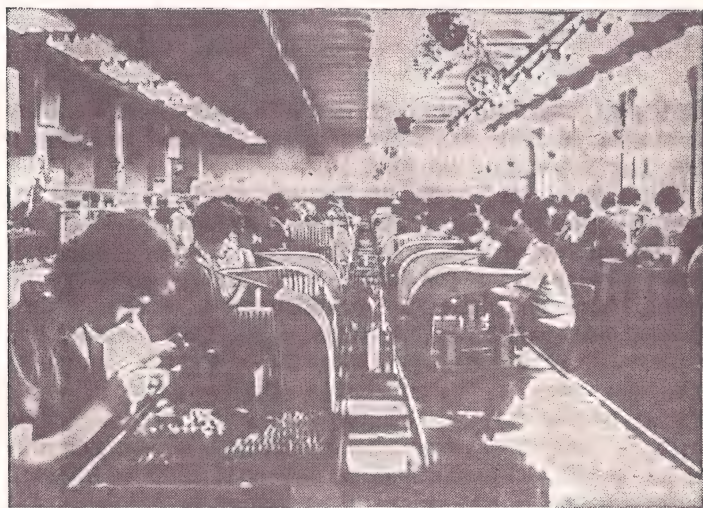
Сборочный конвейер с неподвижными рабочими местами
